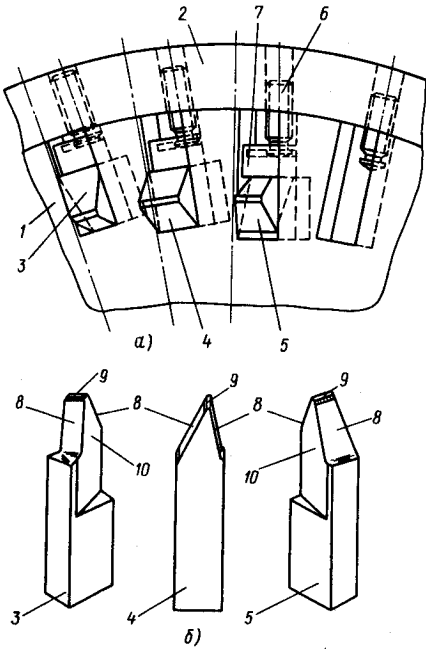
Схема установки острозаточенных резов в корпусе (а) и конструкция резов (б)
